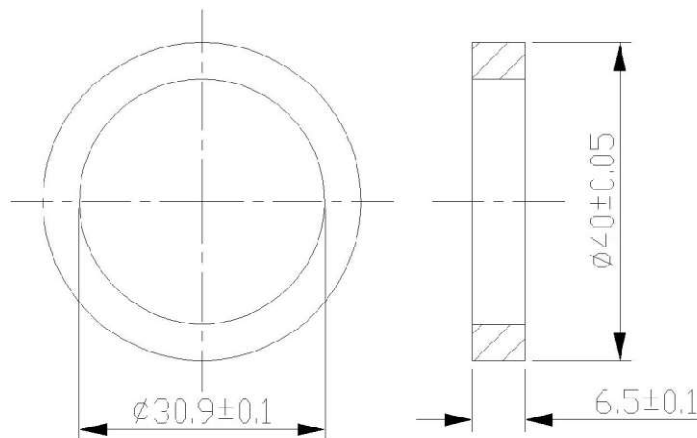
Werkzeug zum Einsetzen der Winkelmanschette
